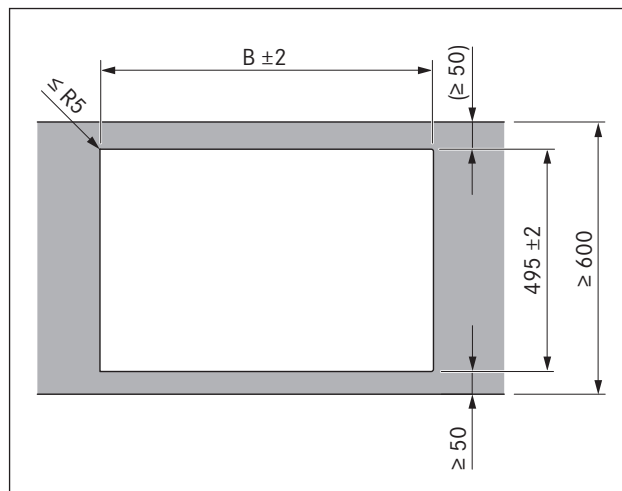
Wielkość zakładki przy montażu z zachowaniem równej powierzchni
